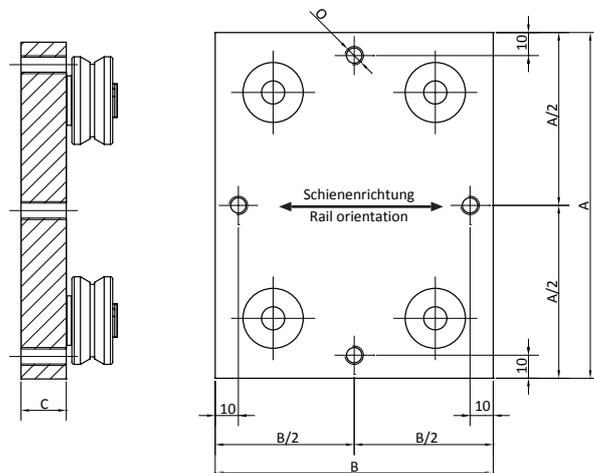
Fertig gebohrte Trägerplatte | Fig.1: Ready drilled carrier plate
